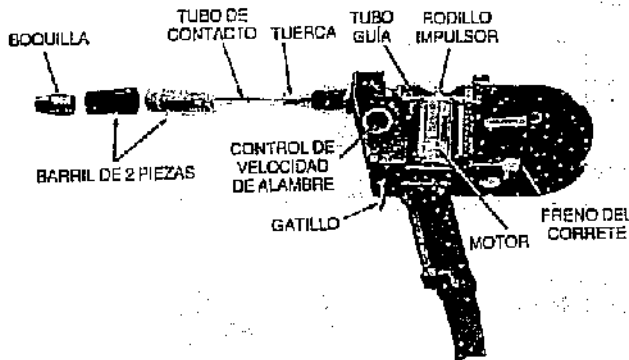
Vista explotada de un soplete del tipo de carrete en la pistola
